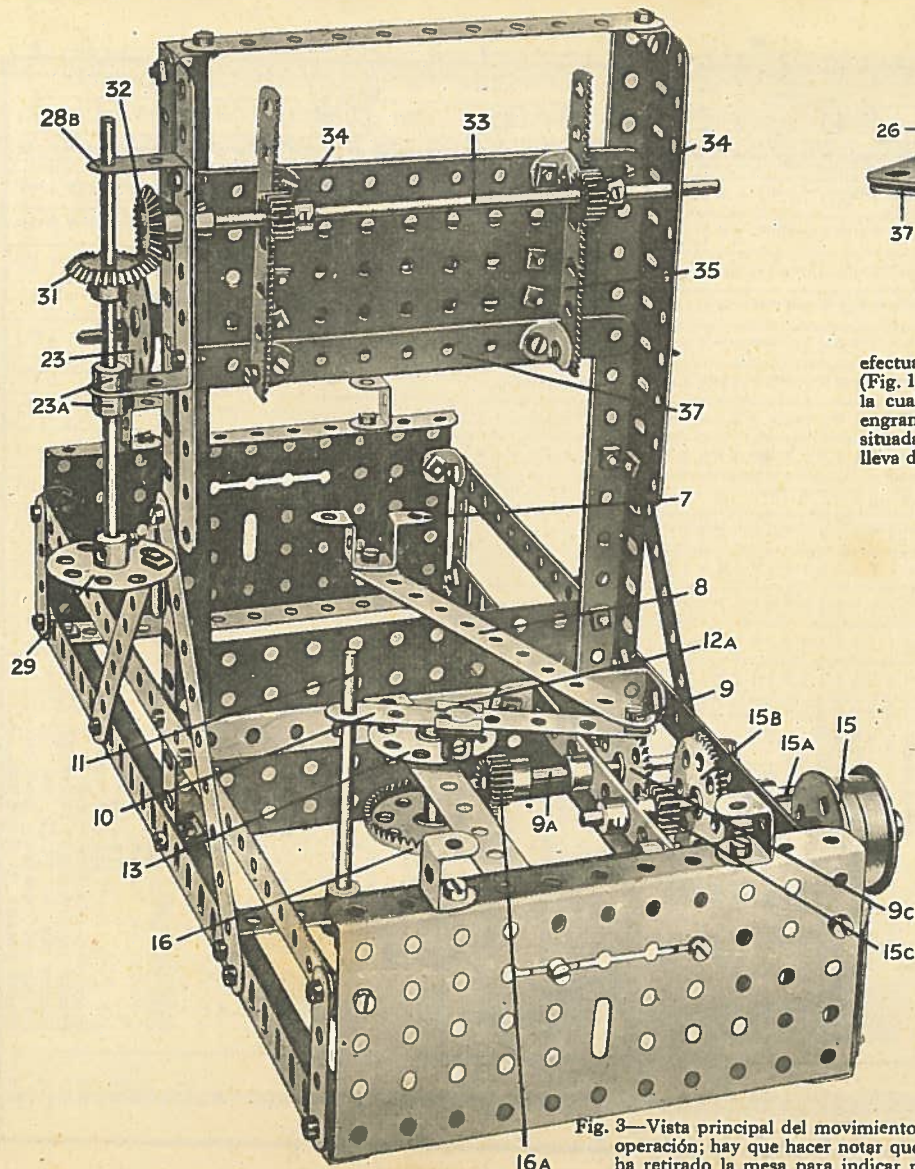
Vista principal del movimiento de operación; hay que hacer notar que se ha retirado la mesa para indicar más claramente el juego de engranajes.
